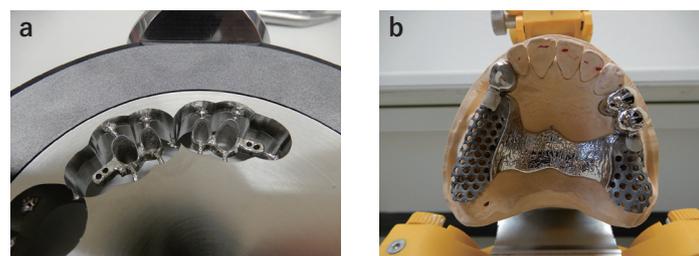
a CNC ミリング後の外冠 b 完成した CAD/CAM ダブルクラウンとフレームワーク
